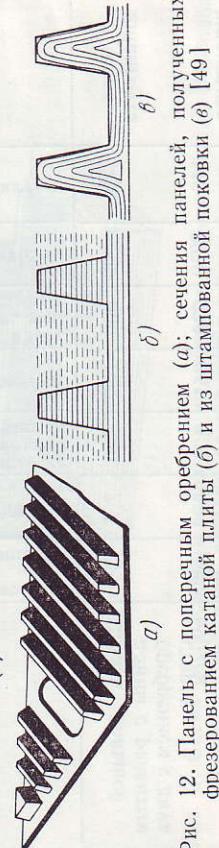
Панель с поперечным обребением (а); сечения панелей, полученных фрезерованием катаной плиты (б) и из штампованной поковки (б) [49]
